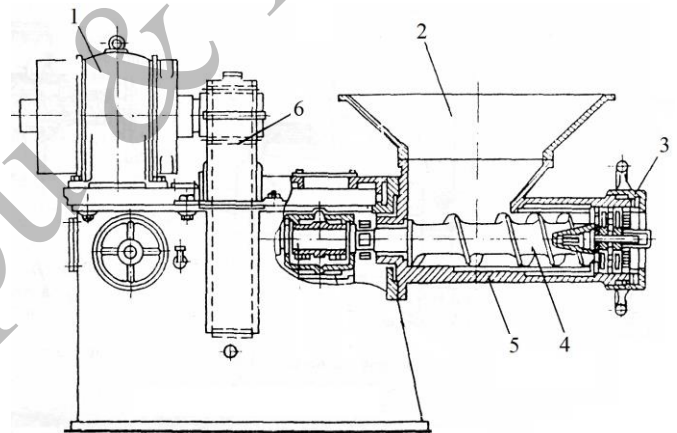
Mașină de tocat carne: 1- motor electric; 2- reductor; 3- mecanism de tăiere; 4- melc; 5- cilindru
